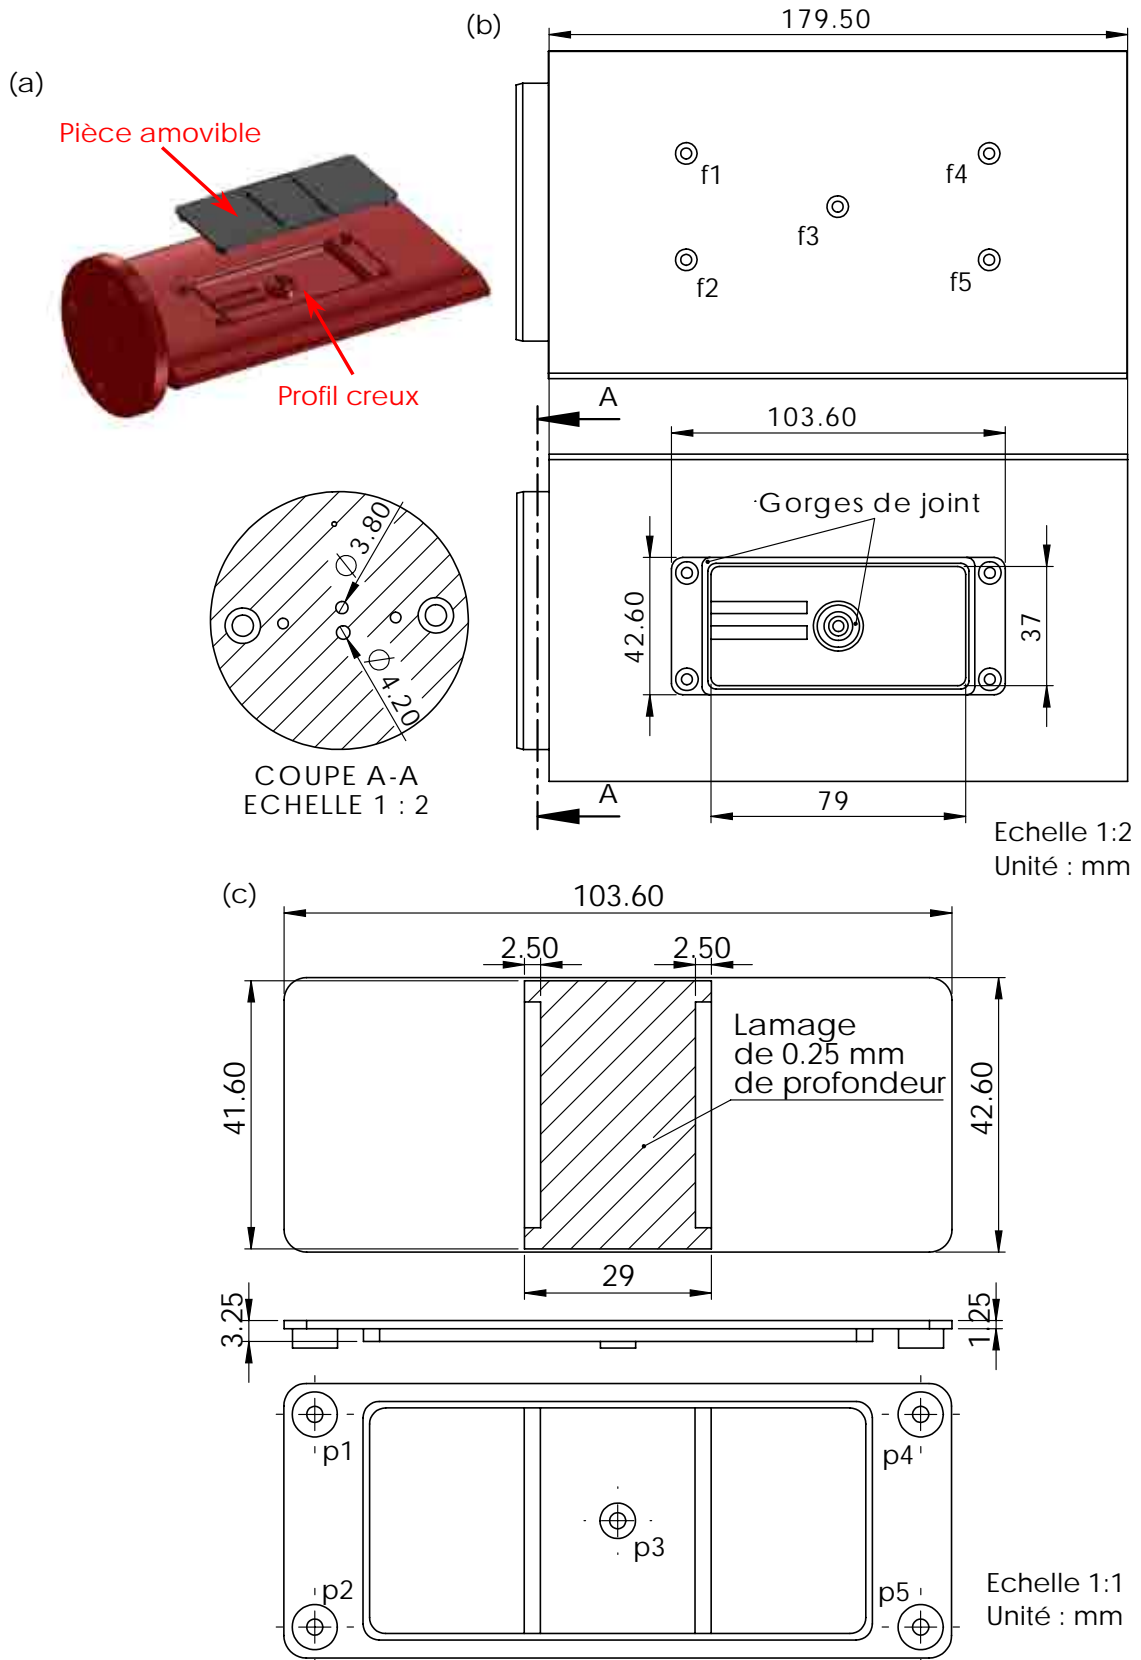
(a) Vue éclatée du profil instrumenté. (b) Dessin technique du profil creux. (c) Dessin technique de la plaque amovible
